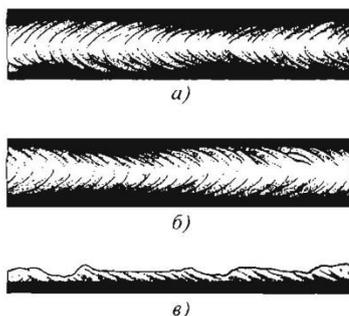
Дефекты формы швов: а – неравномерная ширина шва при ручной сварке; б – то же, при автоматической сварке; в – неравномерная выпуклость – бугры и седловины
